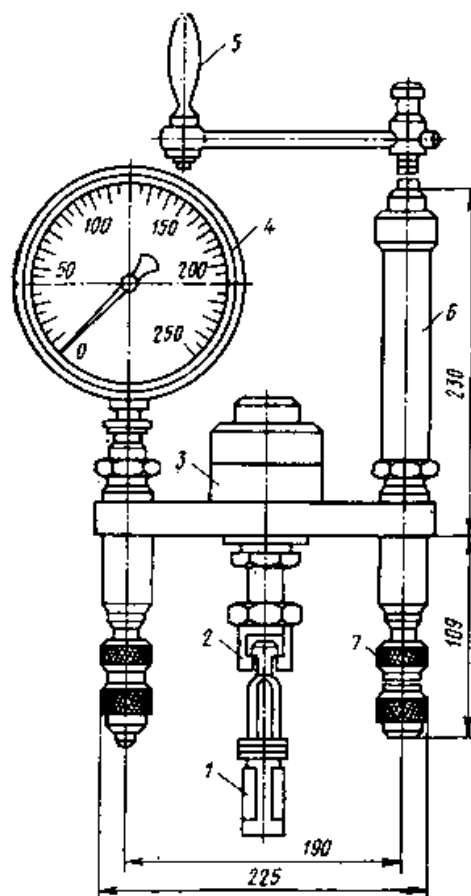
Пресс-насос типа ГПНС-5: 1 – головка анкера; 2 – захват; 3, 6 – гидроцилиндры; 4 – манометр; 5 – ручка; 7 – опоры
